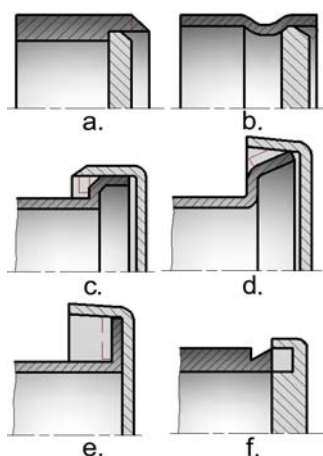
Tipuri de asamblări prin răsfrângere.
